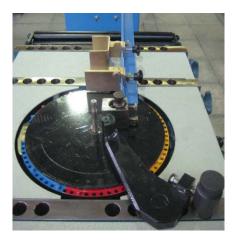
Dispositivo de Estribos Poligonales montado en máquina
